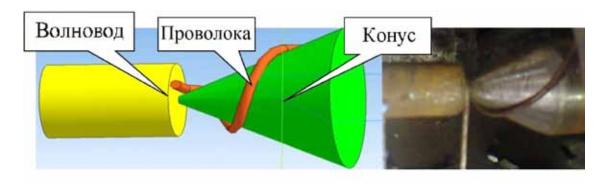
Схема и фотография траектории движения катанки (проволоки) в инструменте, а также схема области схода катанки с ролика
